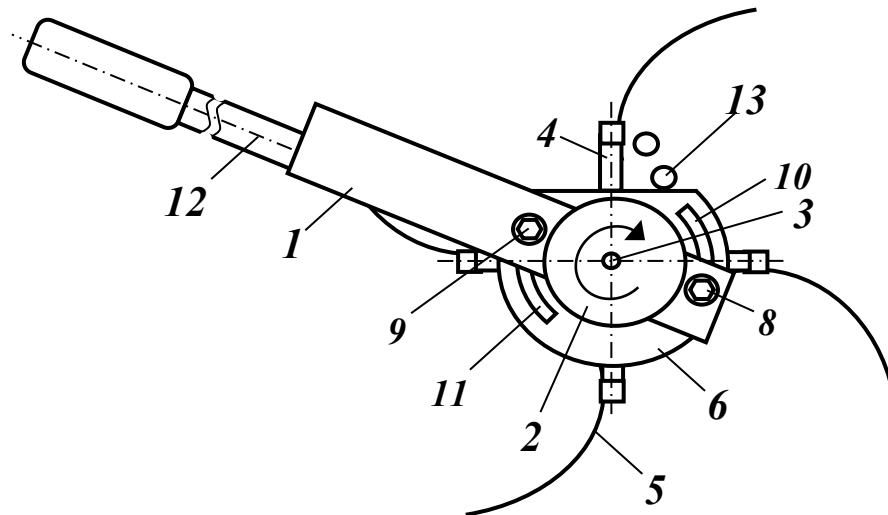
Общий вид устройства (вид сбоку со стороны двигателя)
